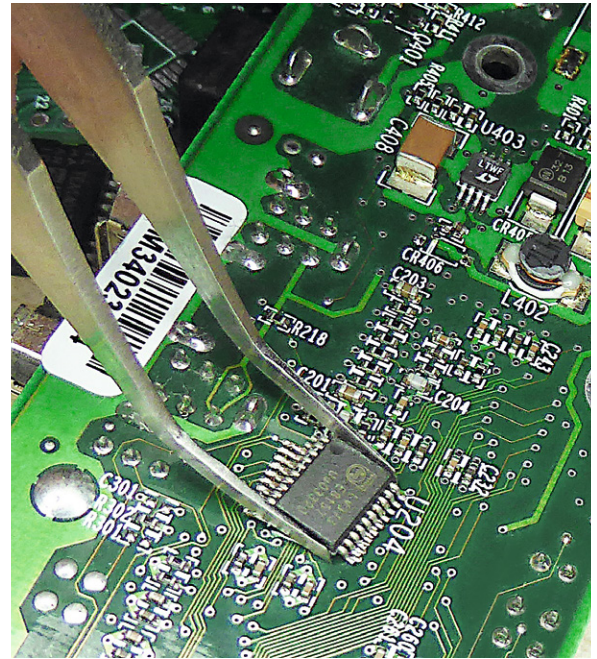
Das mit Heißluft gelöste Bauteil wird mit einer passenden Pinzette vorsichtig von der Platine gehoben.
